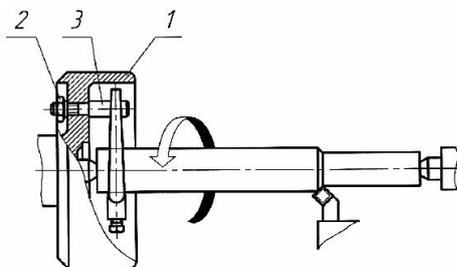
Безопасная планшайба: 1– планшайба; 2– гайка; 3– палец
